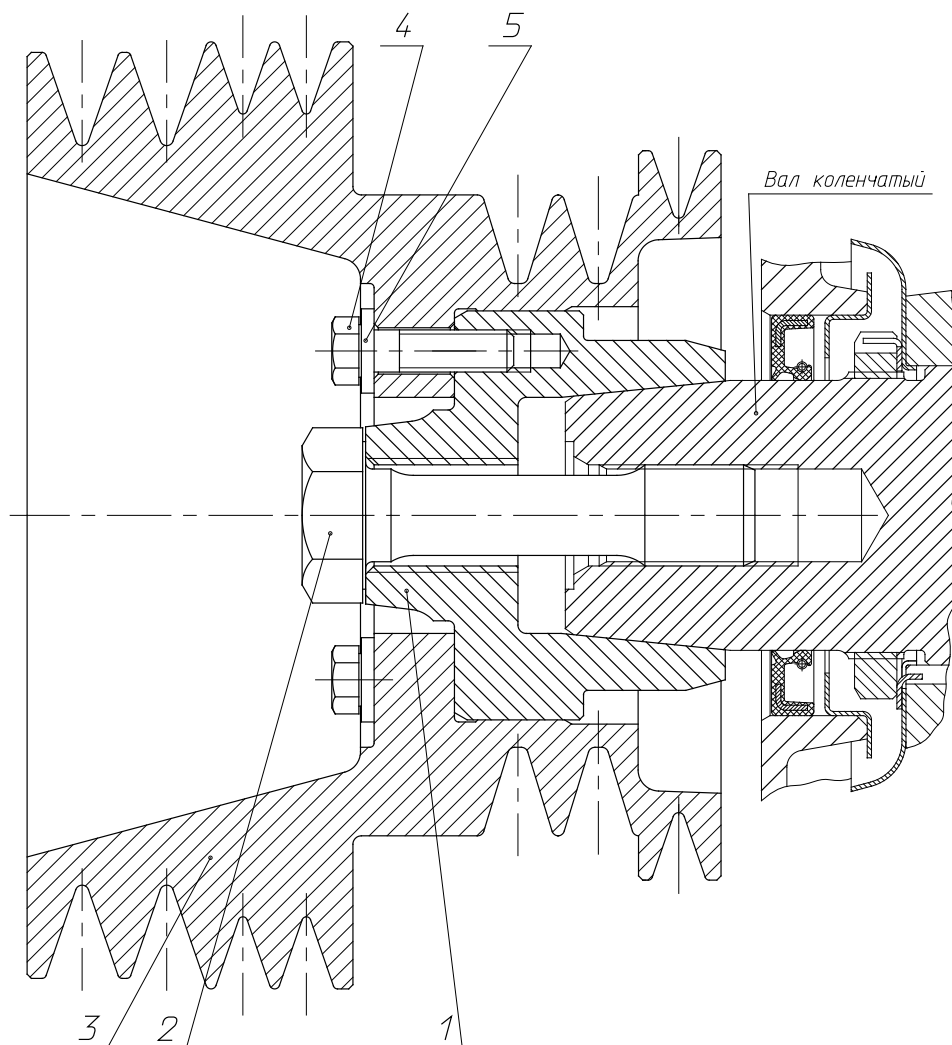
Установка шкива на двигатель, 7601.1005050
